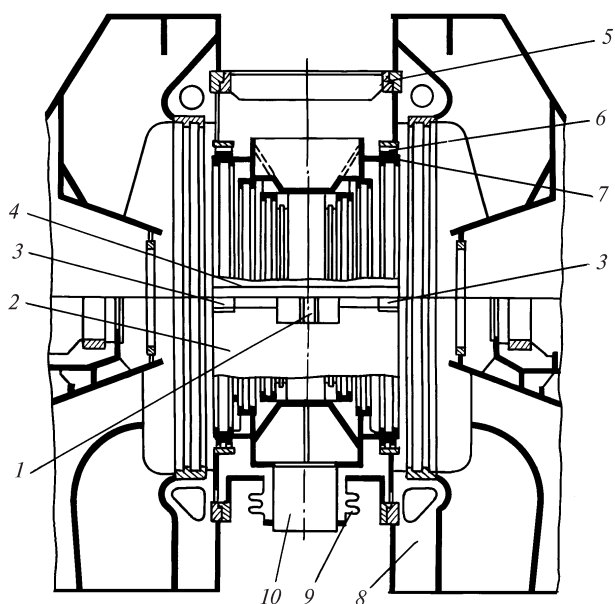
Конструктивная схема двухстенного корпуса ЦНД
